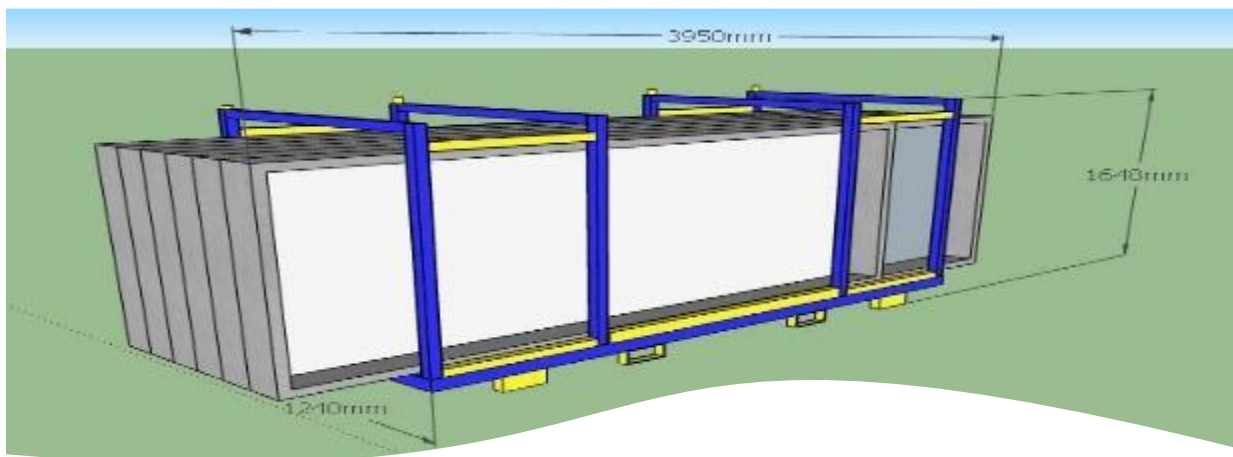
Detalle vista cantidad de paneles. Fuente: Extralum (2019)
